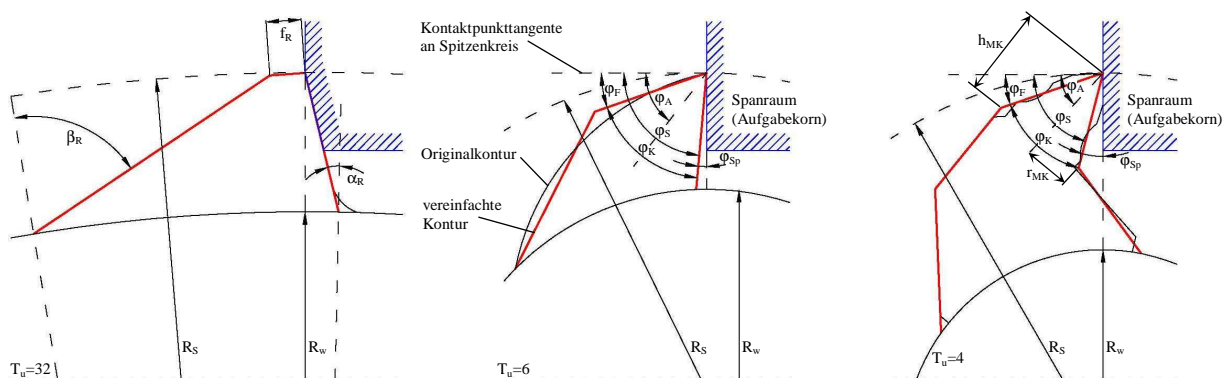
Parameter der Werkzeugmakroform für Riffel (links), Zahn- (mittig) und Meißelwerkzeuge (rechts).
